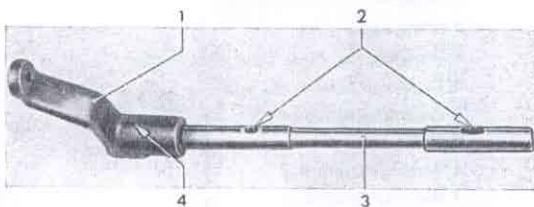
Befestigung Schalthebel an Getriebeschaltwelle
